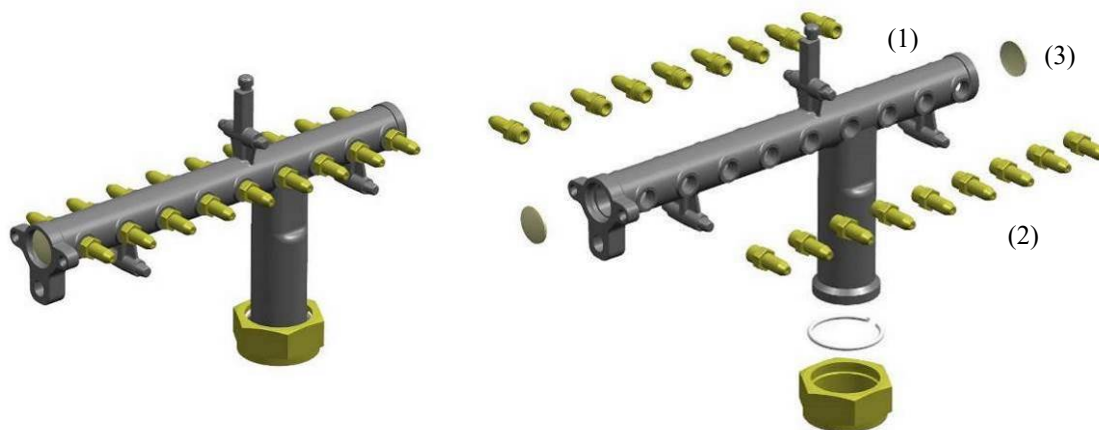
Régua em alumínio extrudida (conjunto montado e conjunto explodido)
